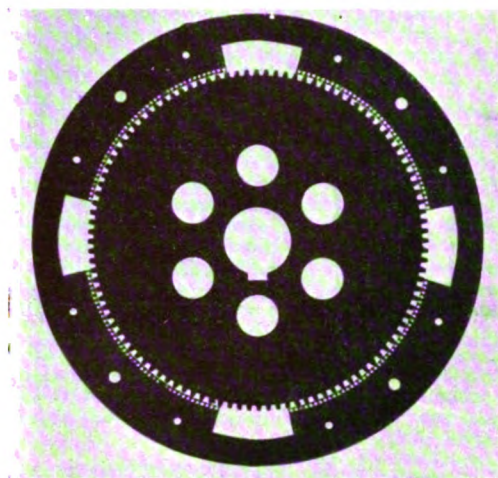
Rotor- und Statorblechschnitt einer 8000 Hz-Maschine (S-Typ).
